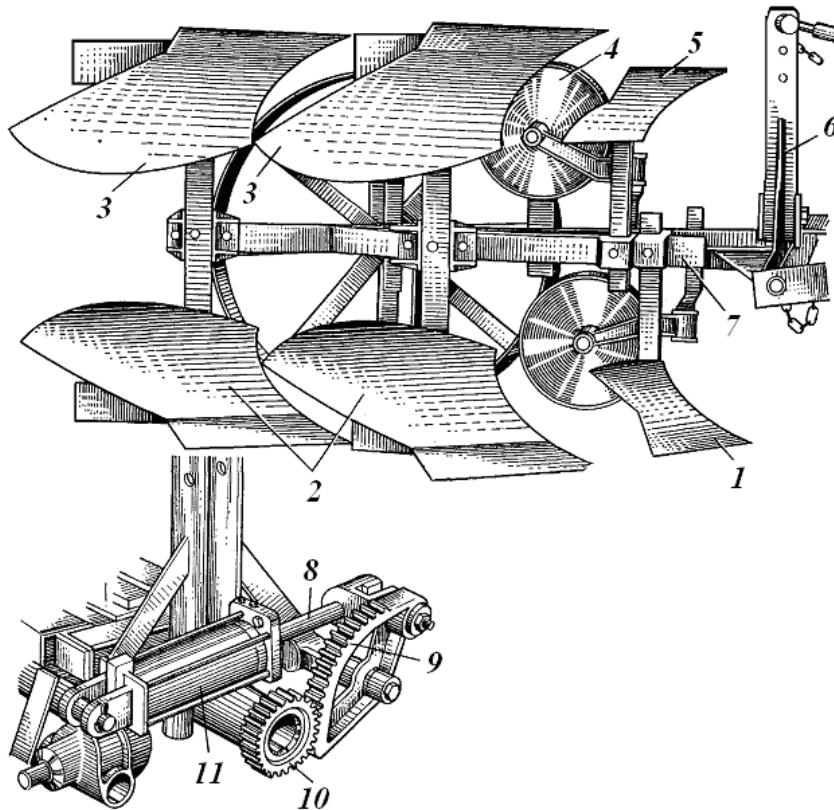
Плуг двокорпусний оборотний начіпний ПОН-2-30: 1 - правооборотний передплужник; 2 - правооборотні корпуси; 3 - лівооборотні корпуси; 4 - дисковий ніж; 5 - лівооборотний передплужник; 6 - начіпний пристрій з механізмом повороту; 7 - рама; 8 - шток гідроциліндра; 9 - зубчастий сектор; 10 - шестерня; 11 – гідроциліндр
